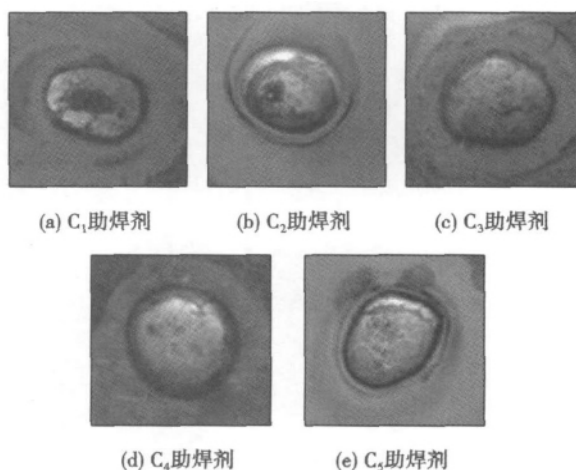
配合 C 组助焊剂时的焊点形貌
